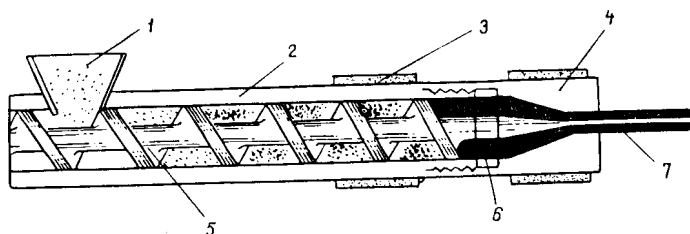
Экструдер (шнек-машина) для получения профильных изделий (труб, стержней и др.): 1 – загрузочный бункер; 2 – цилиндр машины; 3 – нагревательные элементы; 4 – формующая головка; 5 – шнек; 6 – решетка (сетка); 7 – выдавливаемый профиль
